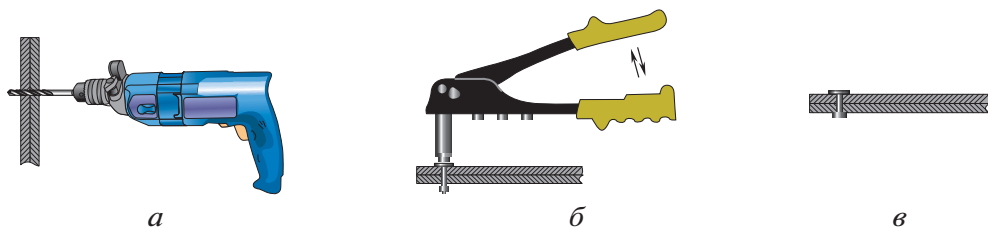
Последовательность соединения заклёпками двух листов металла: *а* — сверление двух листов; *б* — процесс клёпки; *в* — склёпанная заготовка
